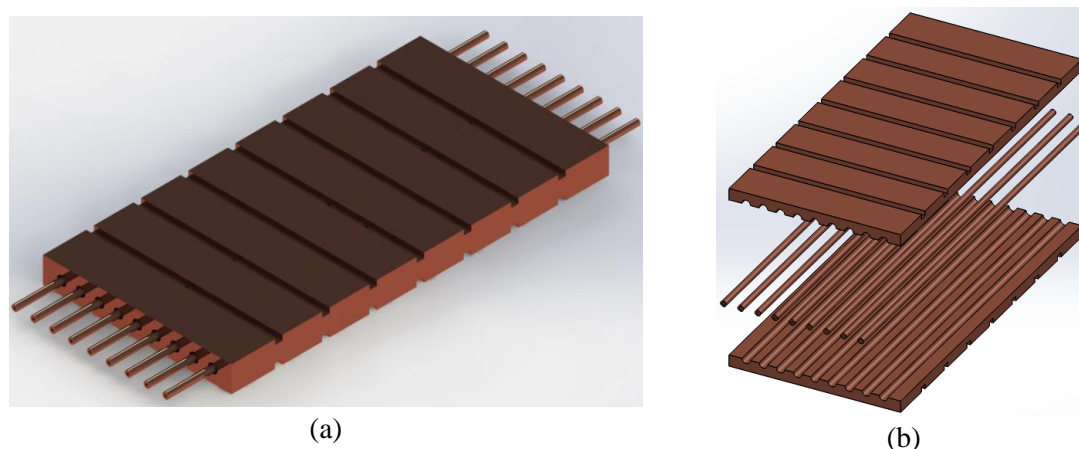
Esquema de fabricação e soldagem da seção de teste: (a) Seção montada e soldada; (b) Seção de teste com vista explodida
